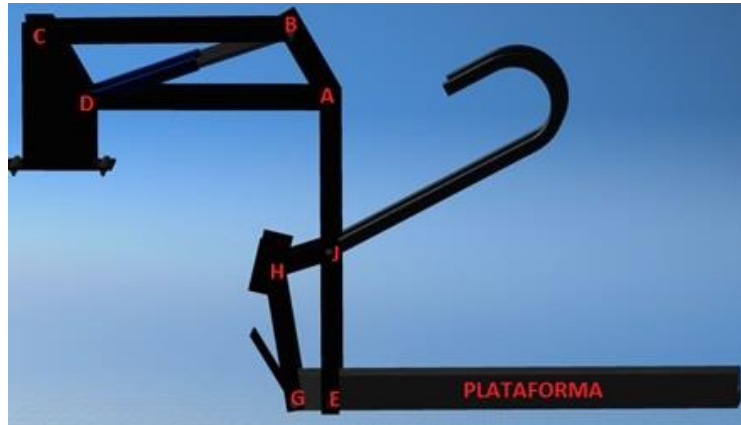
Detalle de los brazos del dispositivo de elevación
